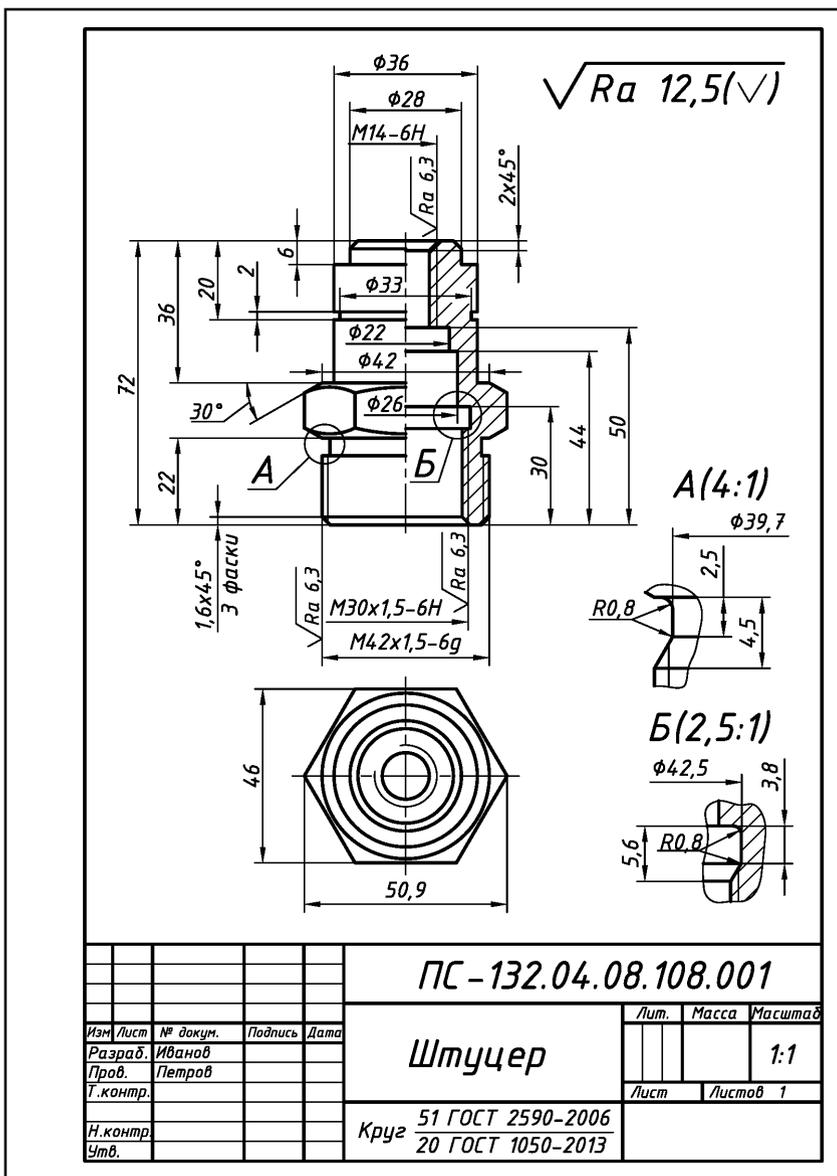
Оформление рабочего чертежа точеной детали из металла
